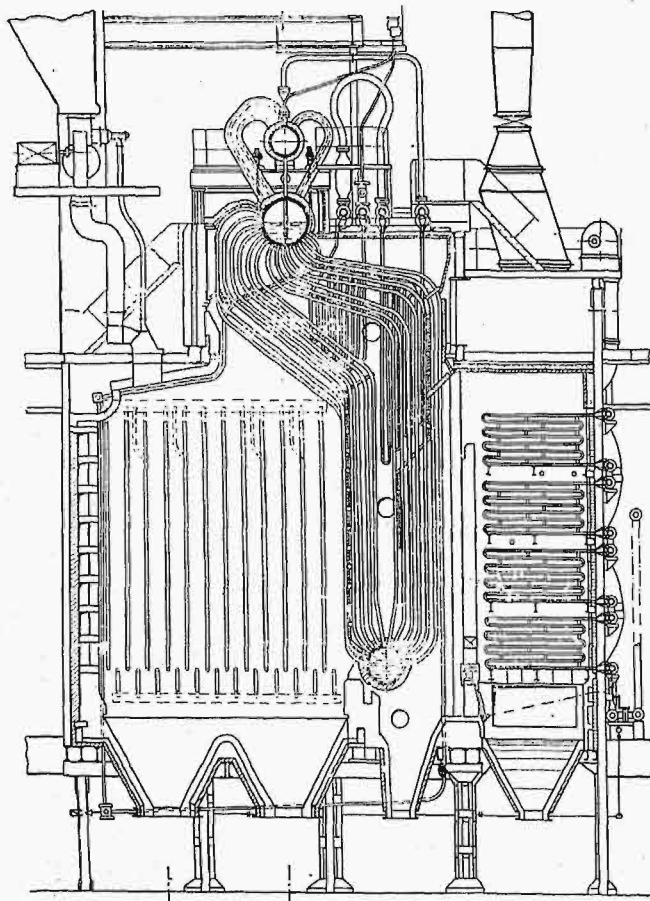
Przegrzewacz syst. Löfflera w zakładach Witkowskich.
